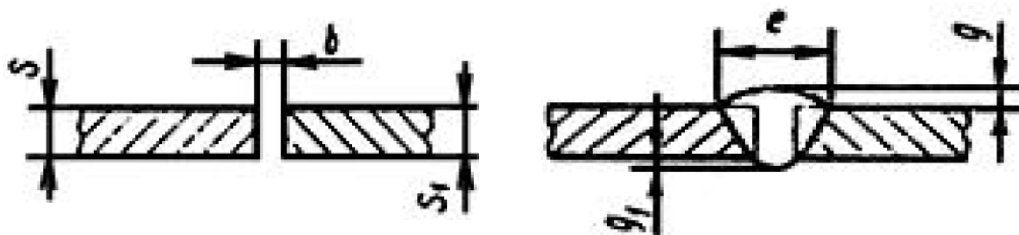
Конструктивний елемент підготовлених кромek виробів, та зварного шва С2
